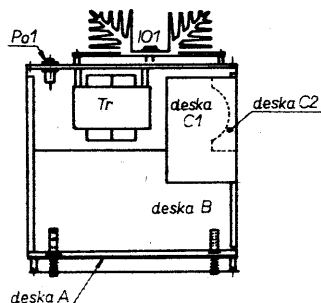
Laboratorní zdroj – pohled ze spodní strany
